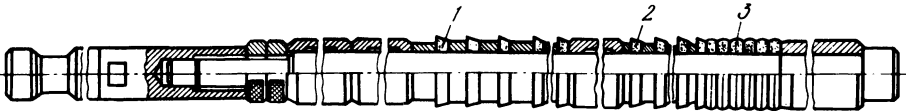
Сборная круглая протяжка с твердосплавными зубьями-кольцами.
